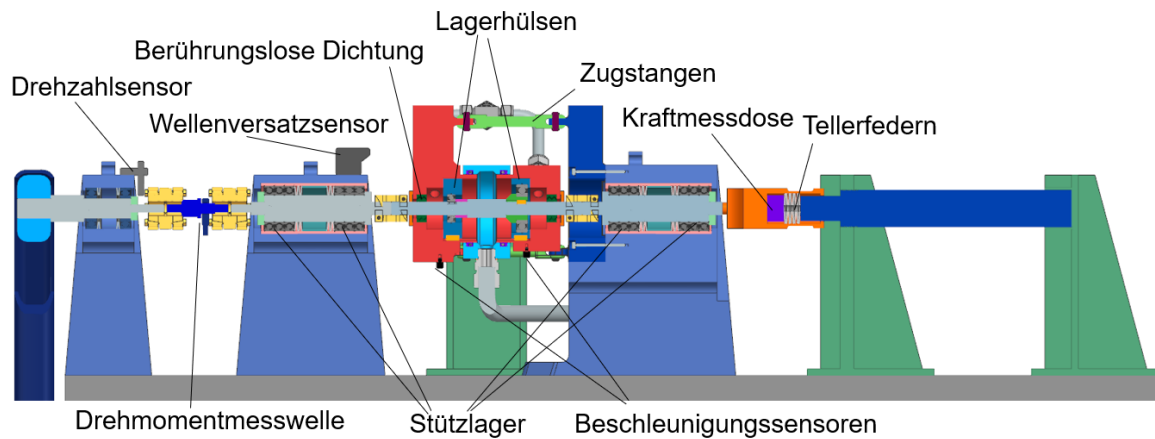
Wellenstrang - Frontansicht - Schnitt
